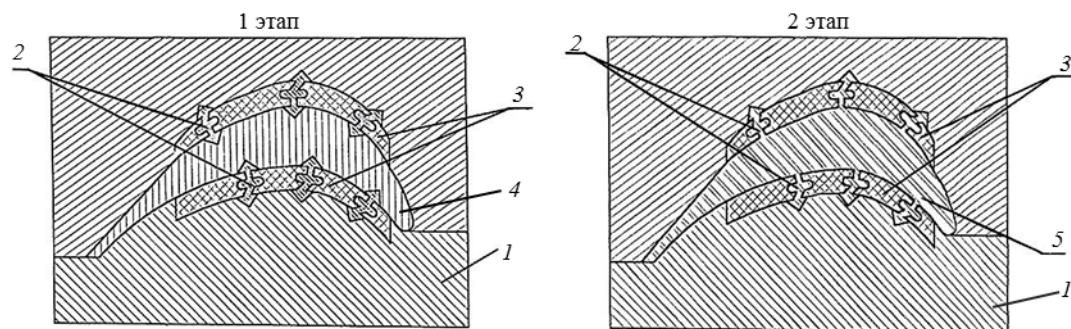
Схема пресс-формы для изготовления промежуточной модели двух секторов:
